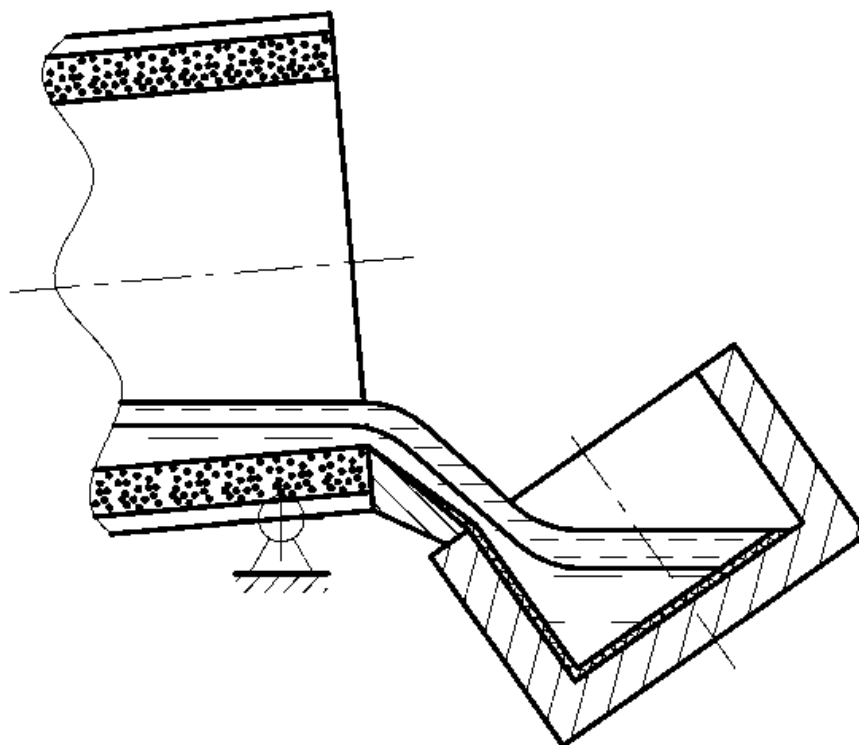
Схема заливки металла при повороте плавильного тигля
